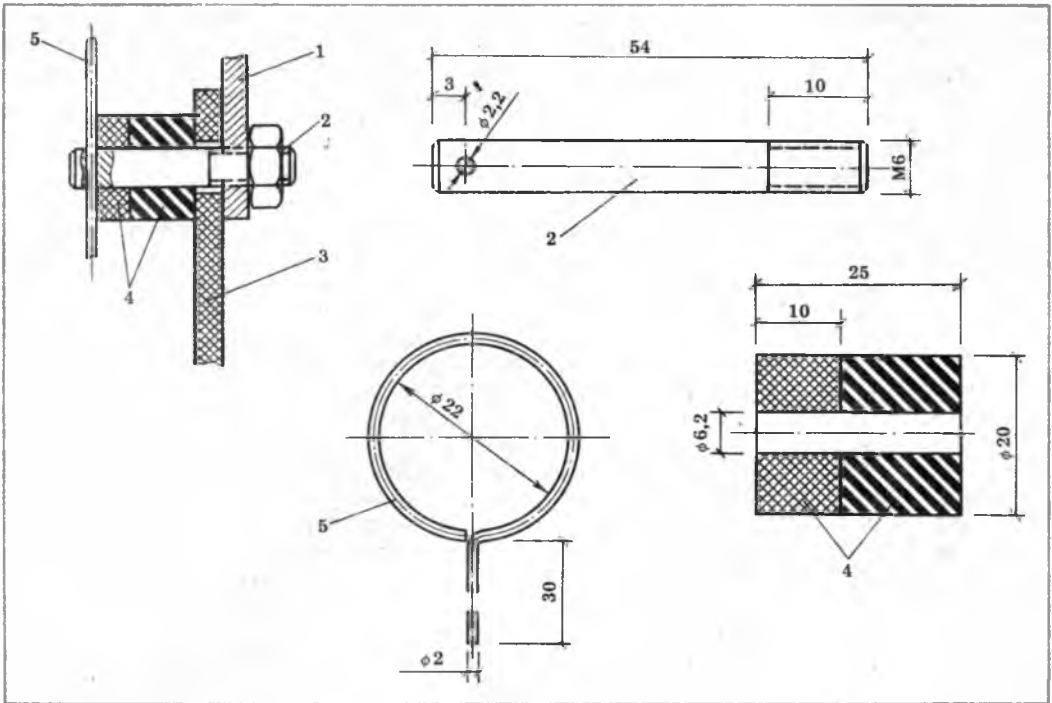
Усовершенствованное крепление крышки люка: 1 — стенка кузова; 2 — шпилька; 3 — крышка люка; 4 — бобышки; 5 — чека
